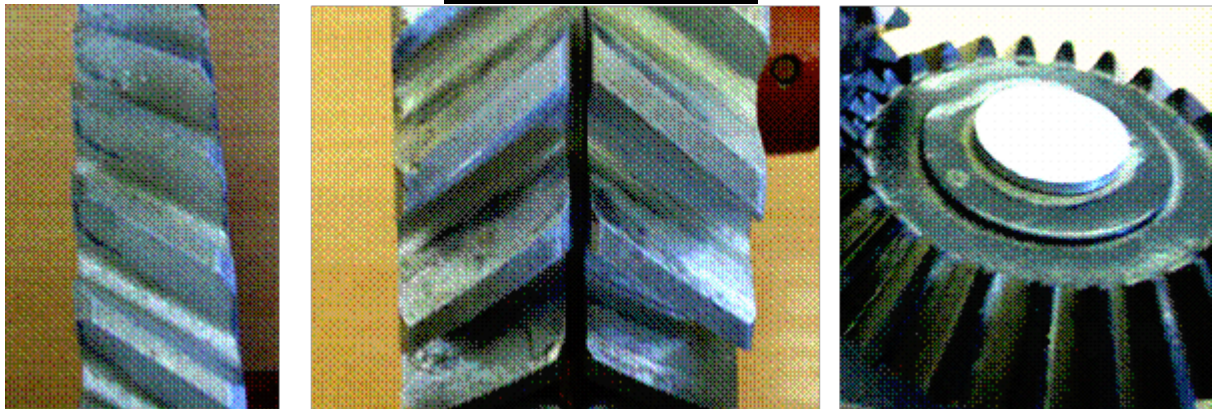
Виды зубчатых колес: цилиндрическое косозубое (слева), шевронное (в центре), коническое прямозубое
